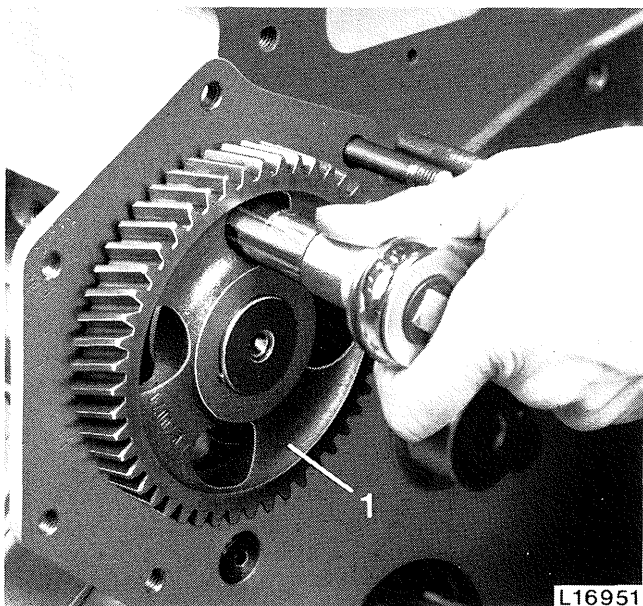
Dépose de la plaque de poussée de l'arbre à cames
